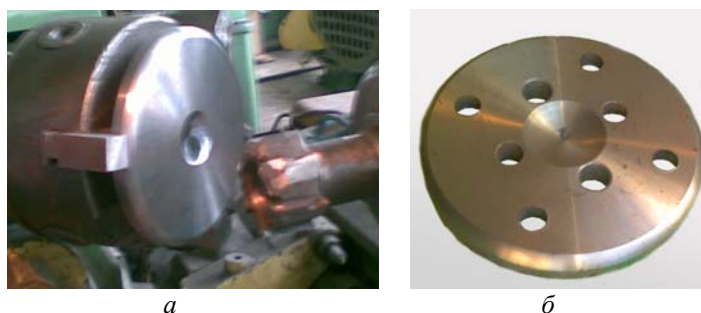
Схема обработки сферической поверхности детали «Подпятник» (а) и вид «Подпятника» (б)
